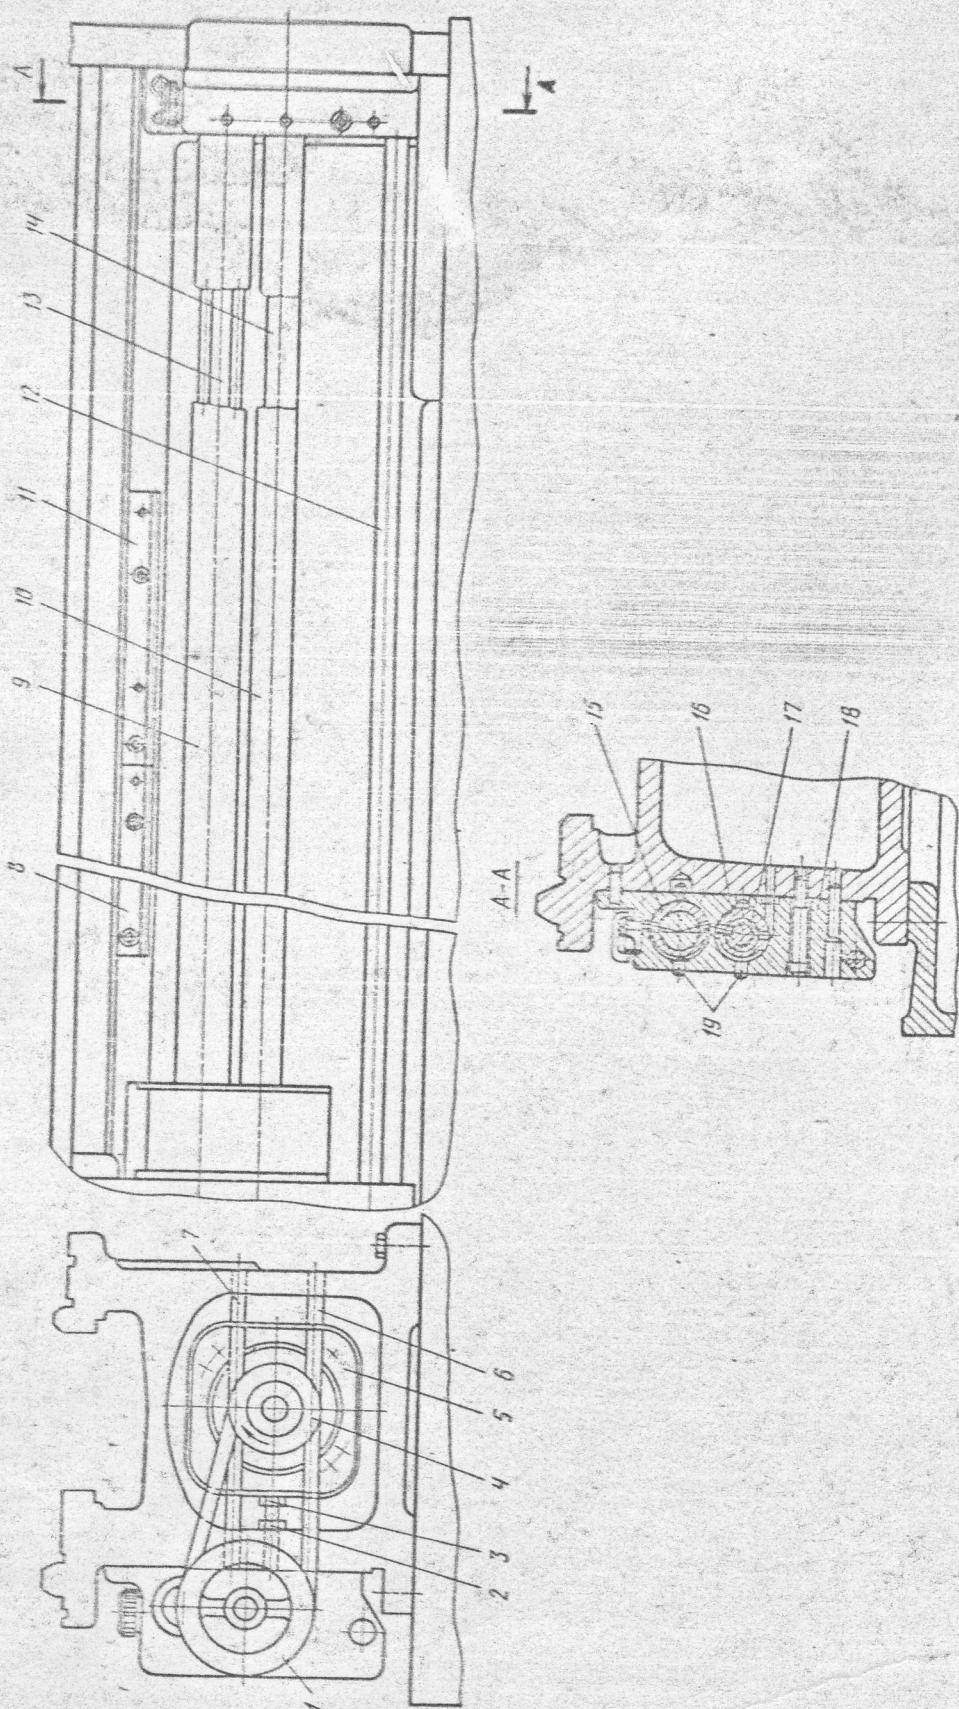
Станина, рейки, ходовой винт, ходовой вал и привод быстрых перемещений суппорта
